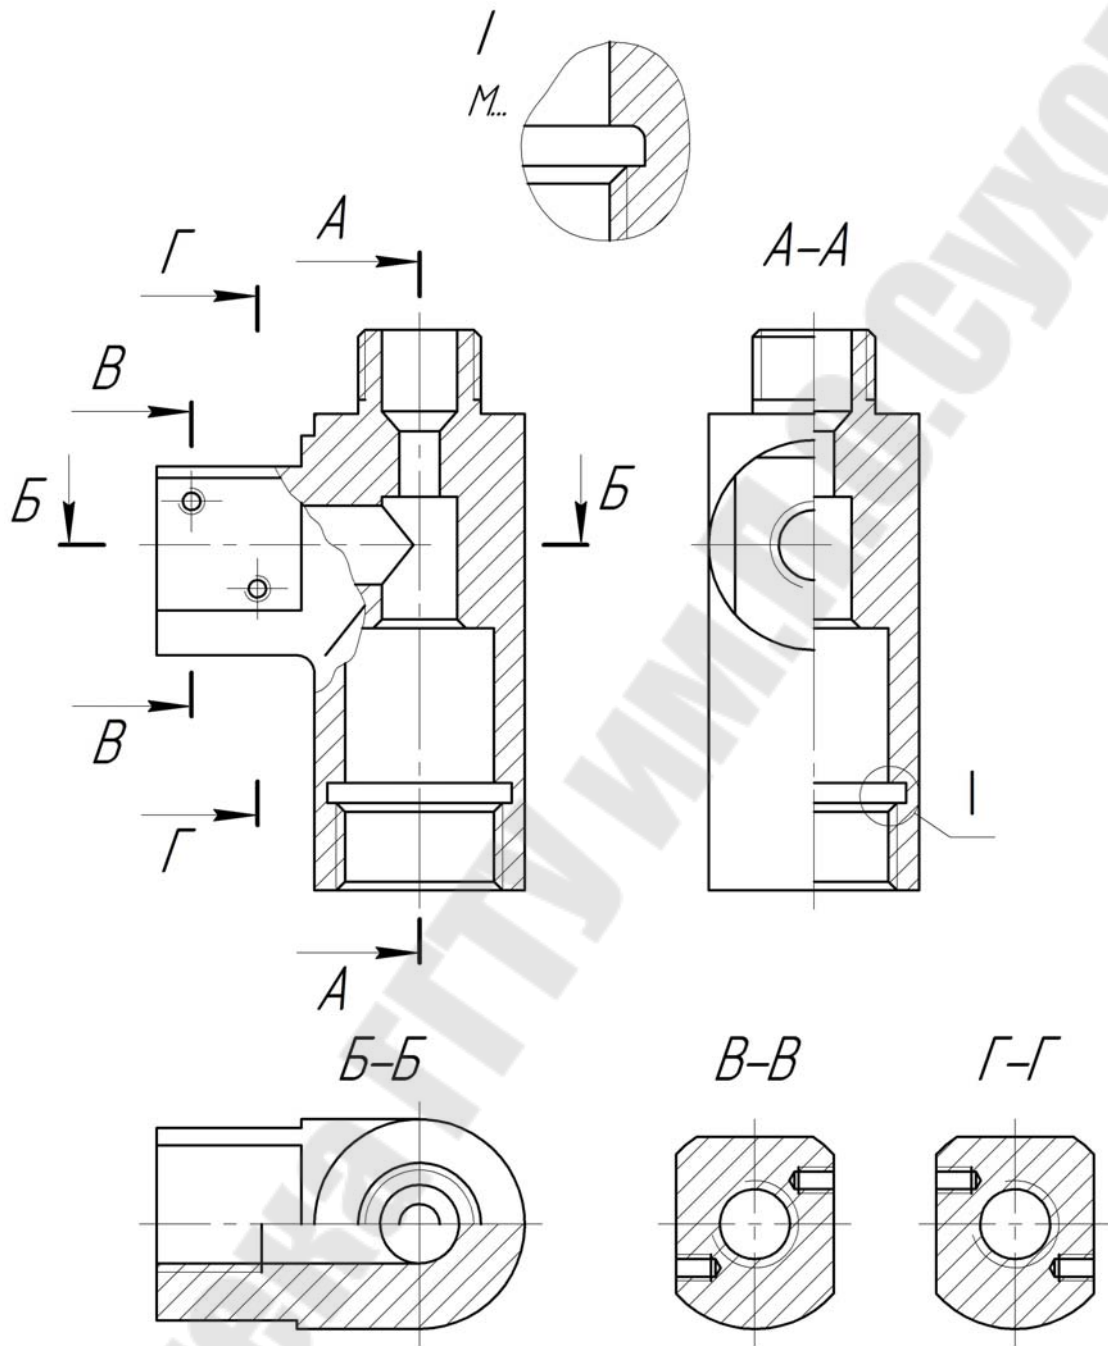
Необходимые виды, сечения и разрезы детали «Корпус»
